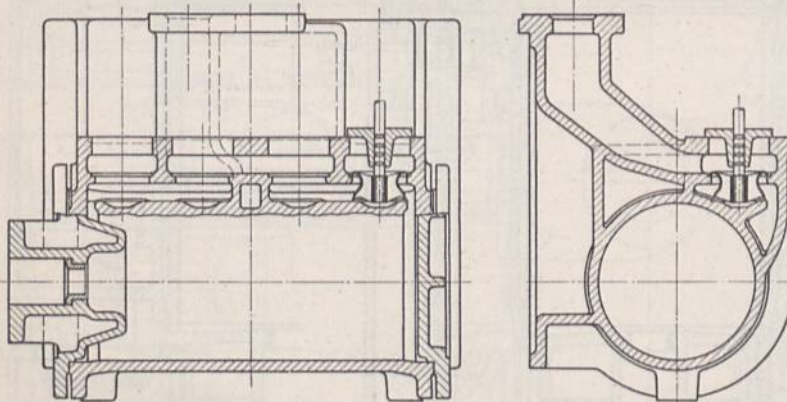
Lokomotivzylinder mit unmittelbar eingearbeiteten Ventilsitzen nach Lentz.
